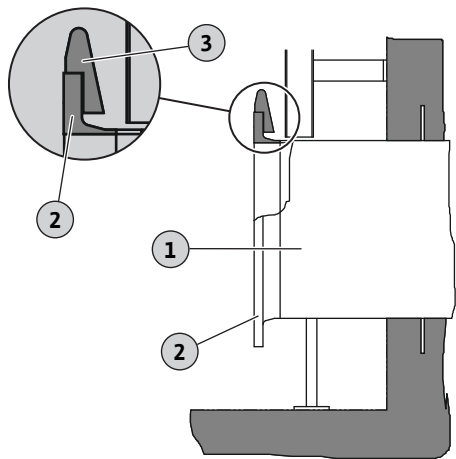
Cunha de pressão: Tubo de pressão com flange de pré-soldagem
